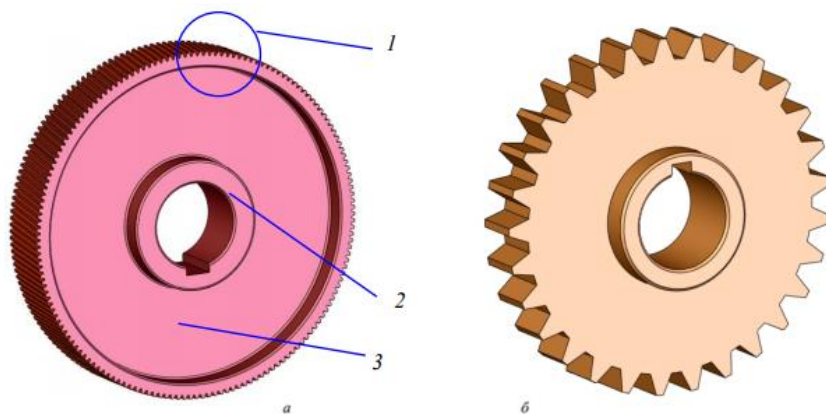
Обобщающая схема конструкции зубчатого колеса (а),
